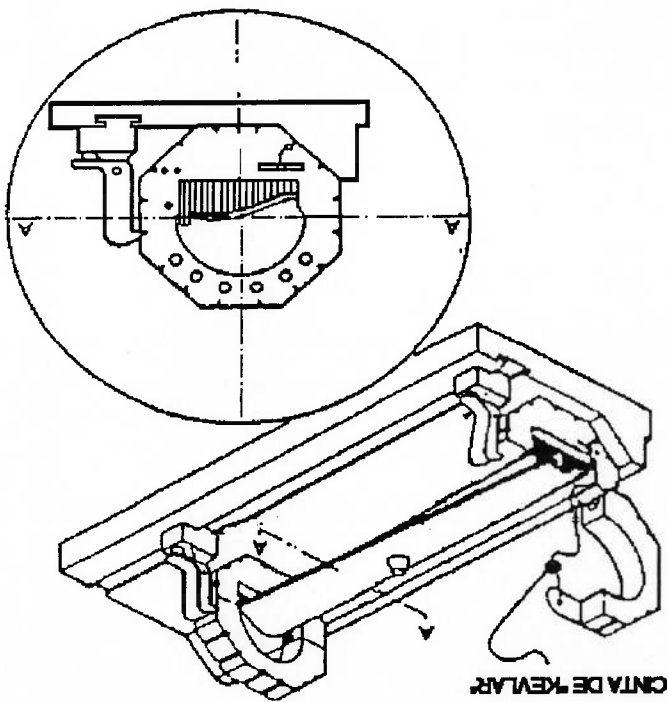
Dispositivo de fixação conformável usado para fixação de pá de turbina
